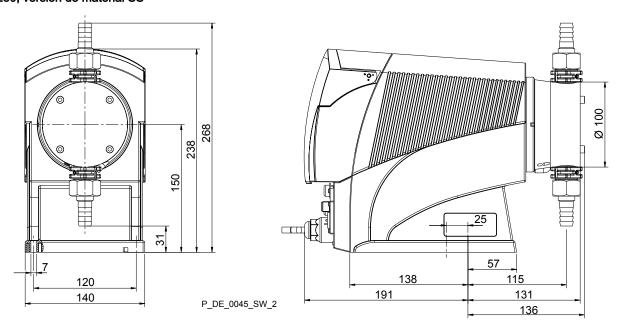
Hoja de dimensiones del tipo delta® 0450 - 0280, versión de material SS; dimensiones en mm
